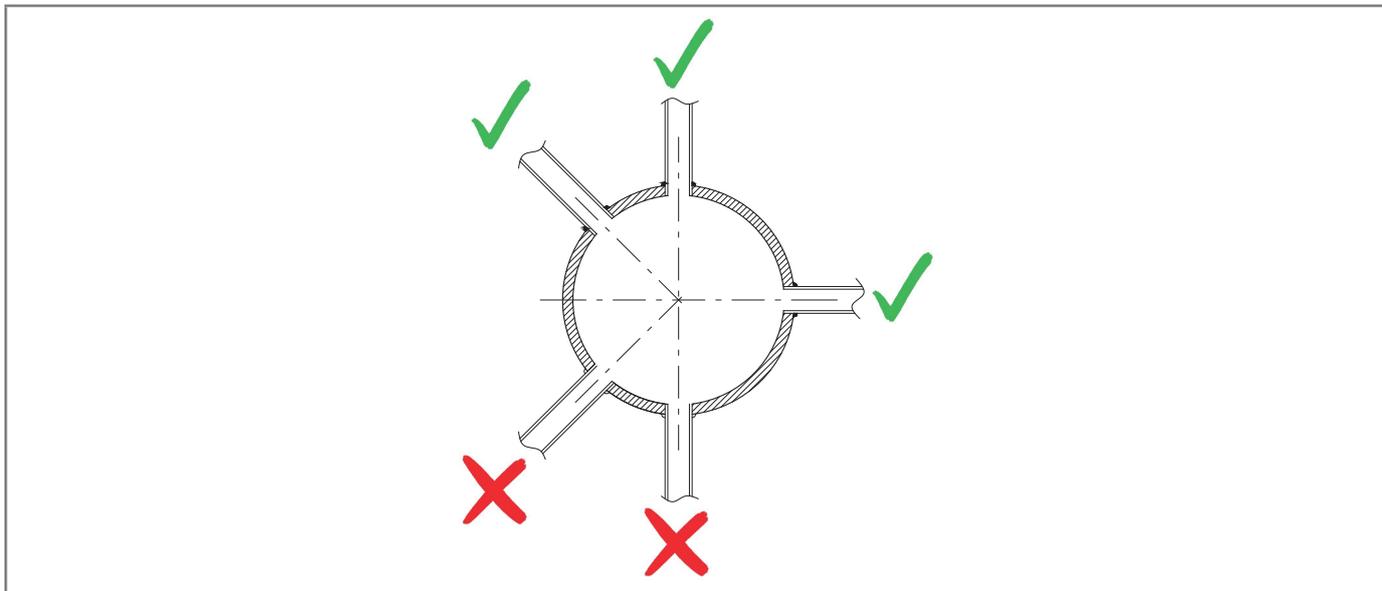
Сварные соединения пневматического соединения
